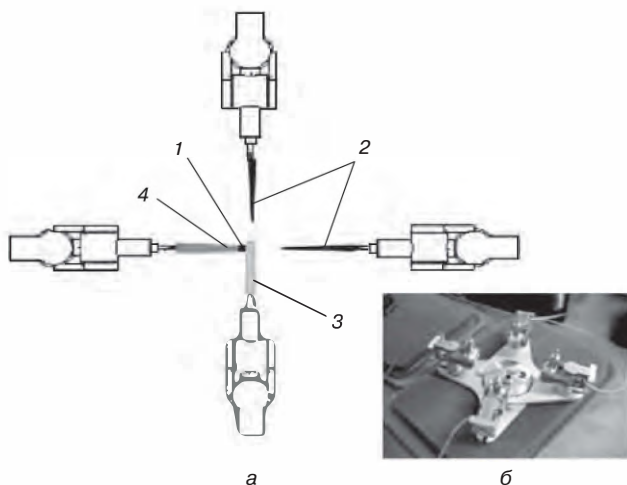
Схема (а) и общий вид (б) приспособления для ковки микрозаготовок Ni_3Al : 1 – заготовка размером 0,3–0,5 мкм; 2 – манипуляторы; 3 – наковальня; 4 – молот [I.79]
